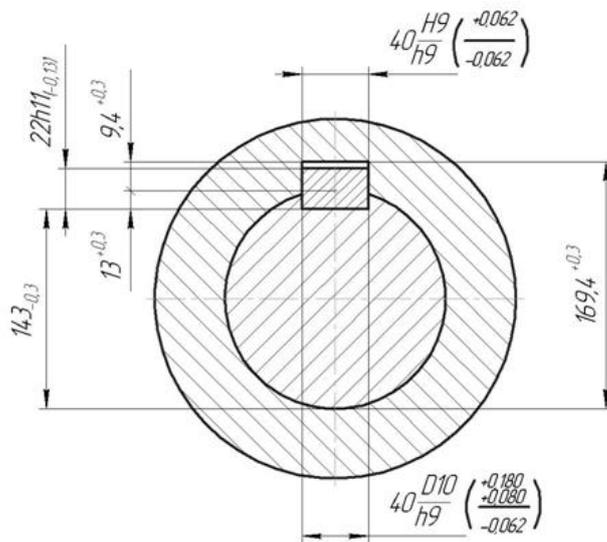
Ескіз деталей шпонкового з'єднання
